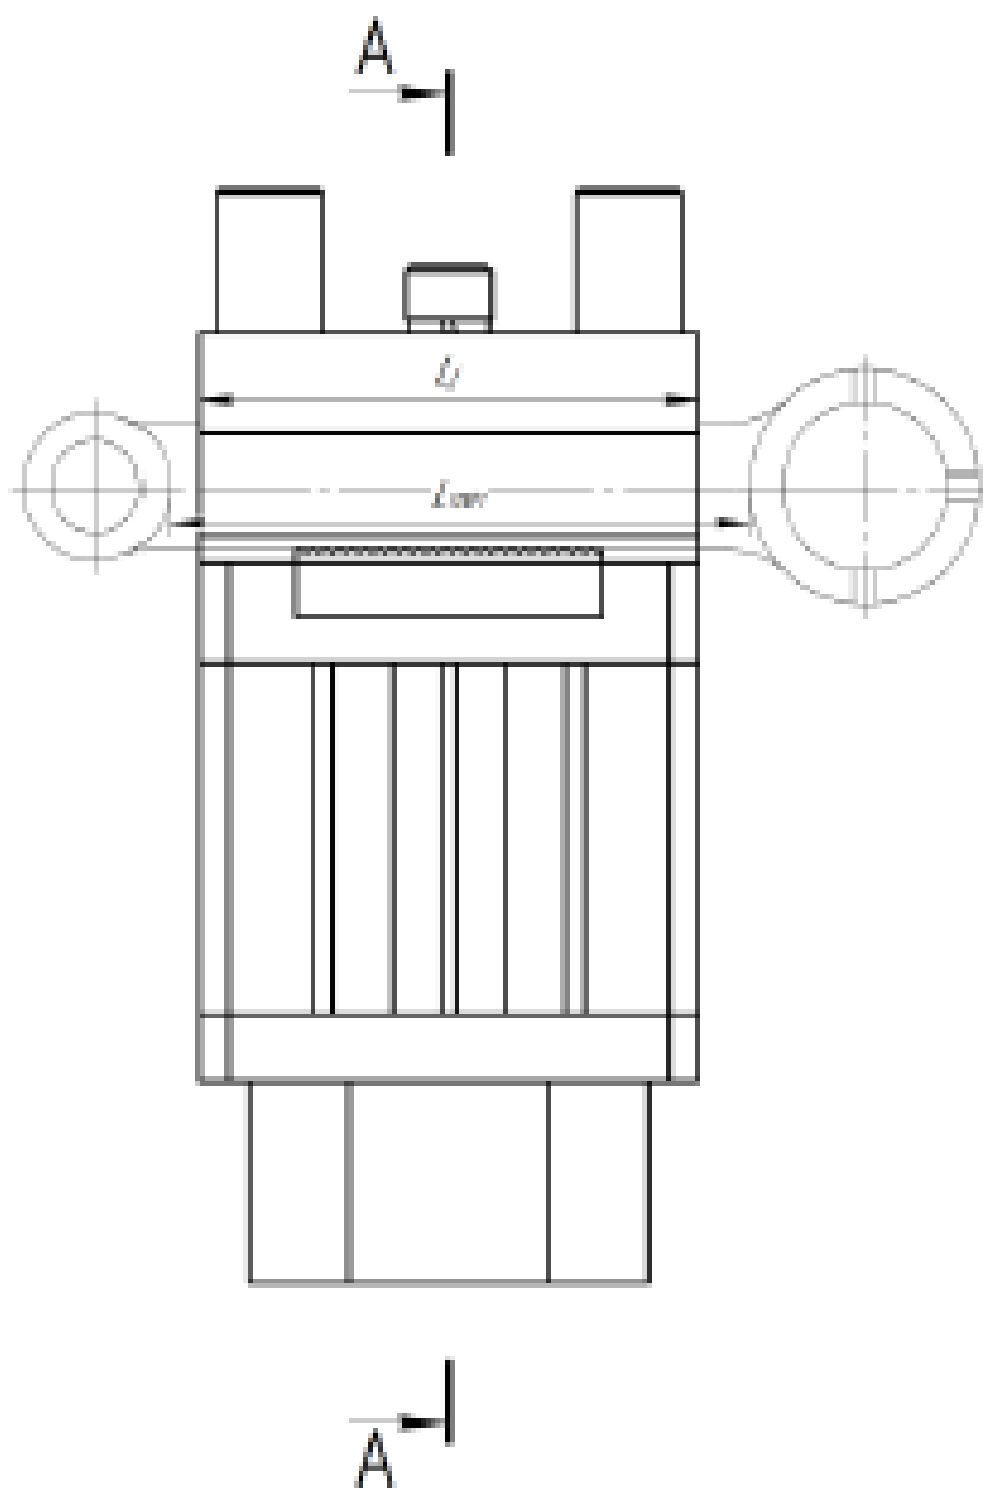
Граничні габаритні розміри деталей, які можливо встановити в даний верстатний пристрій з мінімальними розмірами [204]
